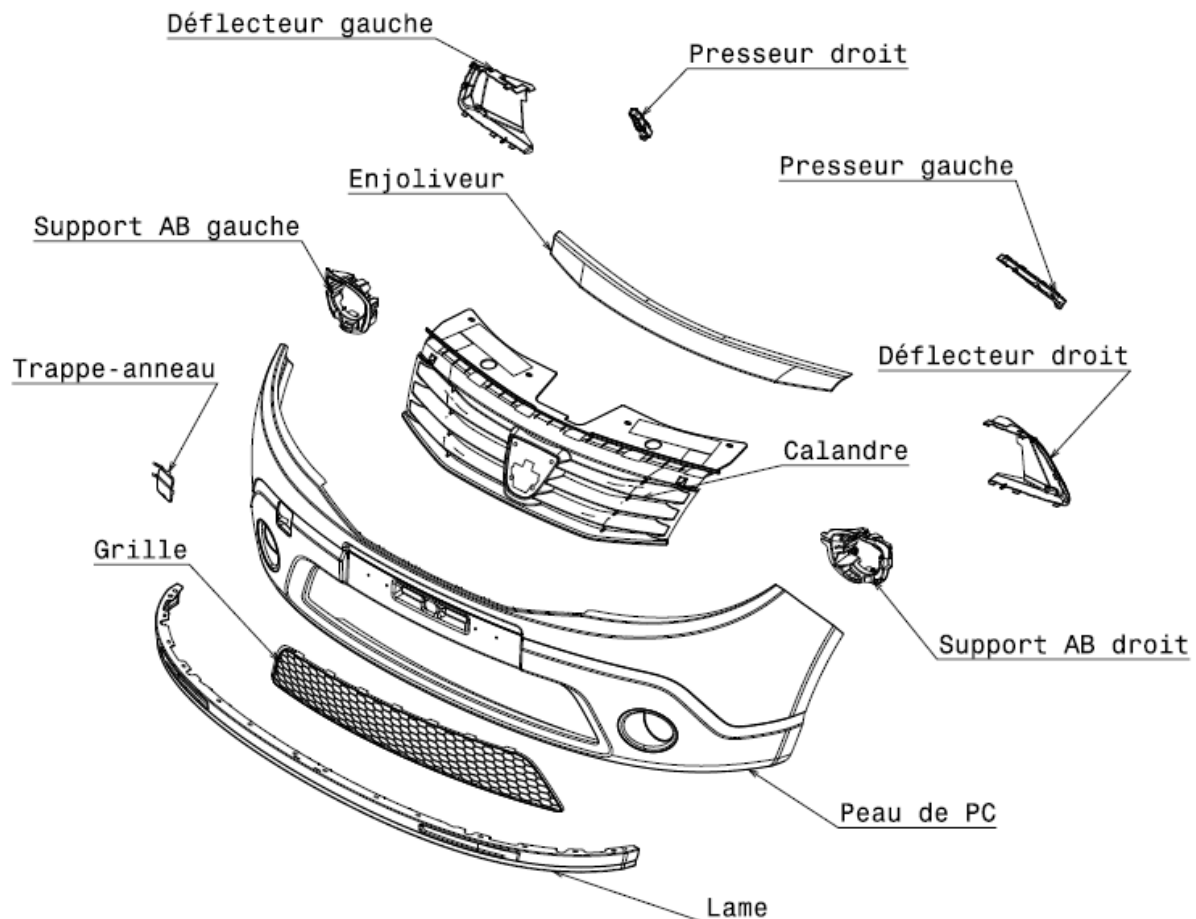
Vue éclatée du produit PC 1 composé de 12 pièces une fois le travail réalisé
